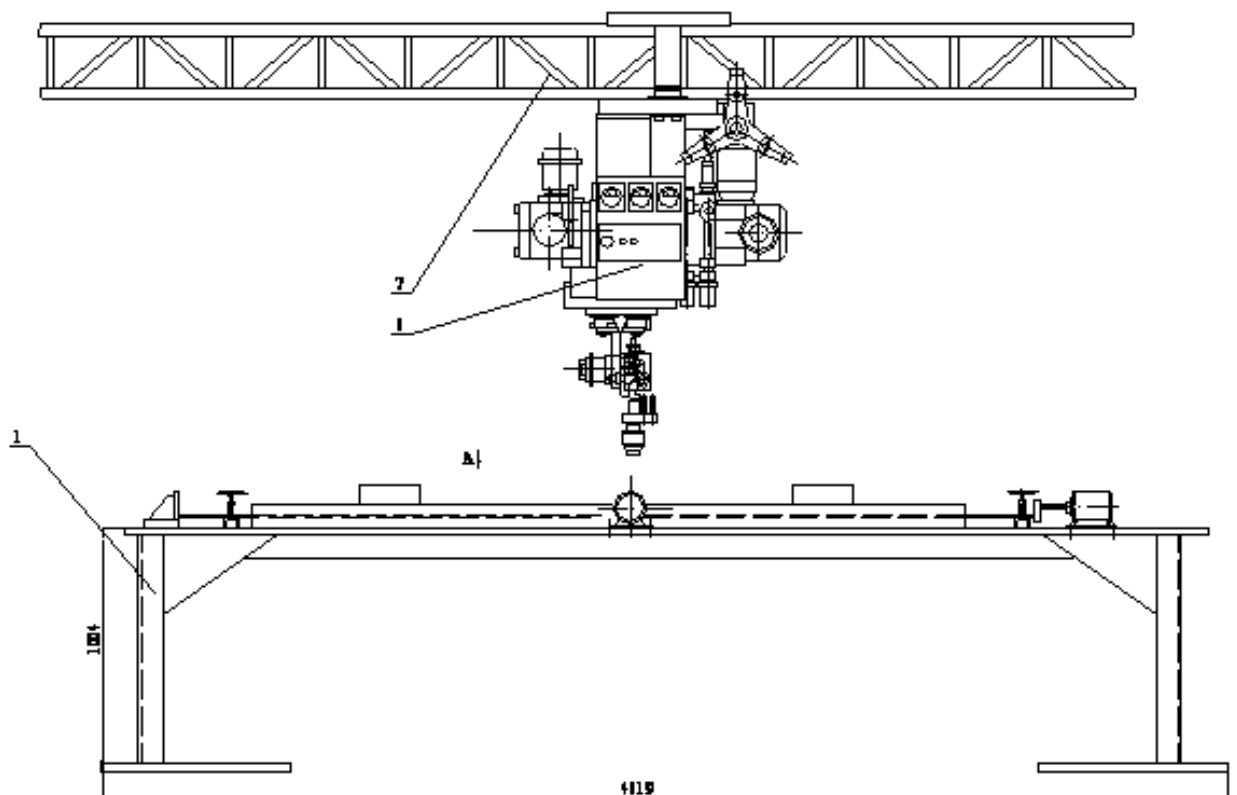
Установка для зварювання поздовжніх швів.
